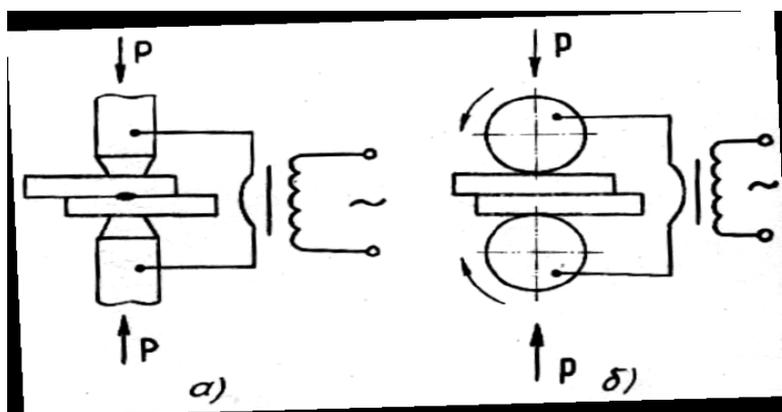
Схемы точечной (а) и роликовой (б) сварки
